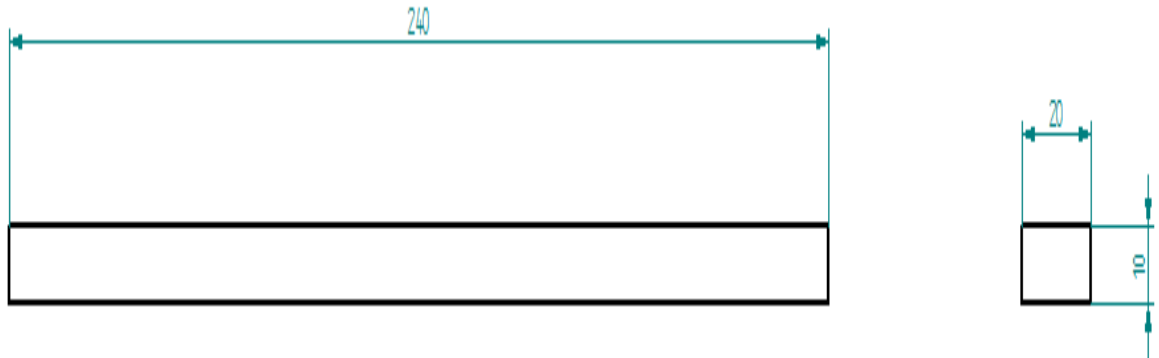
Dimensiones probeta flexión. (fuente: autores proyecto)
